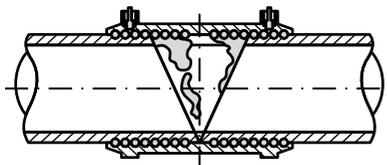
Unsachgemäße Verschweißung
